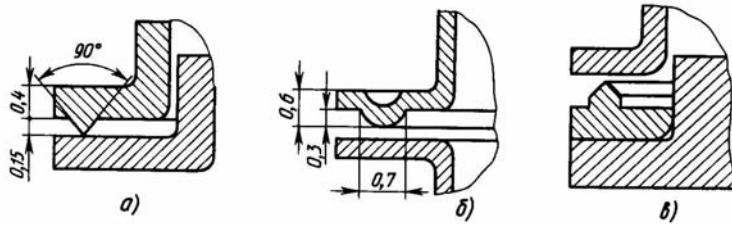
Варианты выполнения рельефа для контактной сварки
